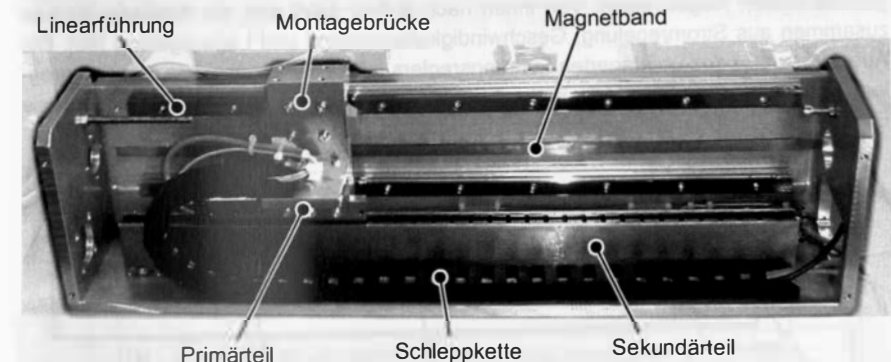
Prototypischer Aufbau der Verlegeeinheit mit Linearmotor
